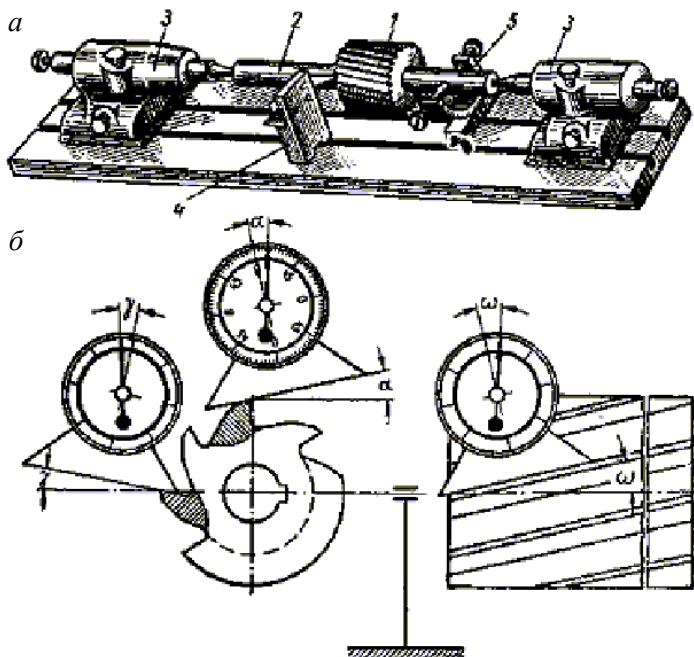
Установка для измерения углов зубьев фрезы маятниковым угломером:
